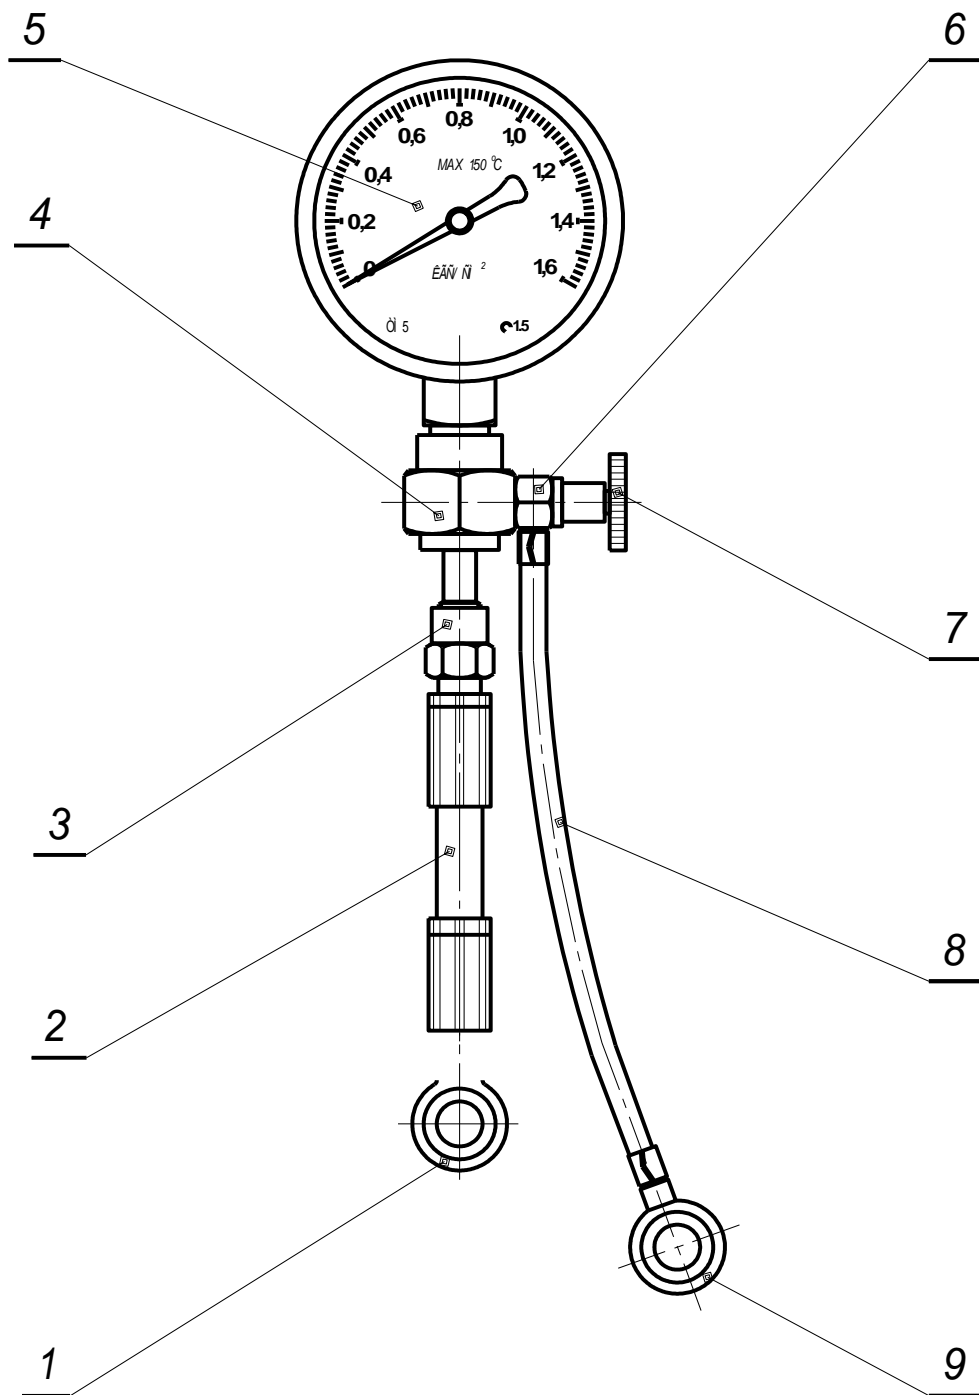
Дизельтестер ТАД-01НД: 1, 9 – наконечники рукавов; 2 - топливоподводящий рукав; 3 - корпус клапана; 4 - корпус манометра; 5 – манометр; 6 - корпус вентиля; 7 - винт вентиля; 8 - сливной рукав
